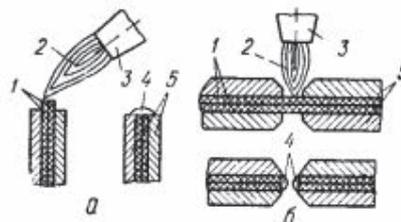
Схема сварки пленок оплавлением кромок: с подготовкой свариваемых кромок (а) и без подготовки свариваемых кромок (б): 1 – свариваемые пленки, 2 – струя газа, 3 – наконечник нагревателя, 4 – сварной шов, 5 – зажимные губки
